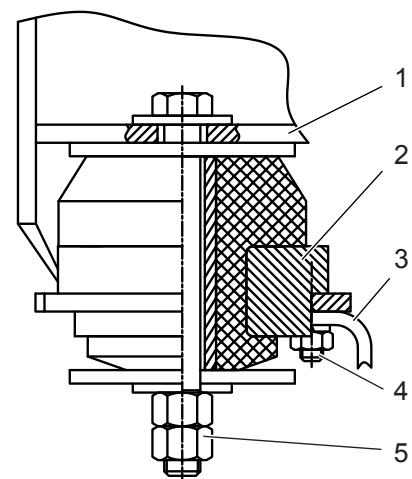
Опора силового агрегата с двигателем Weichai
